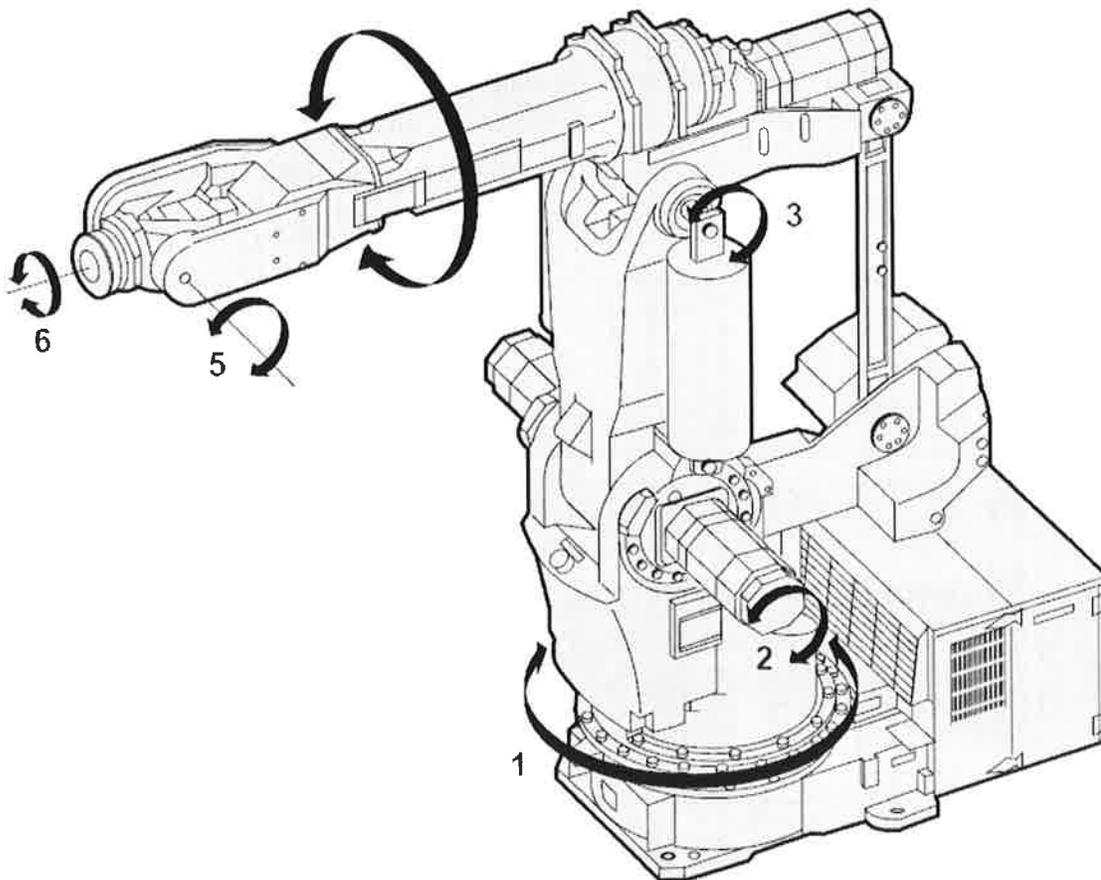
Vista isométrica del robot Fanuc S-420 i
